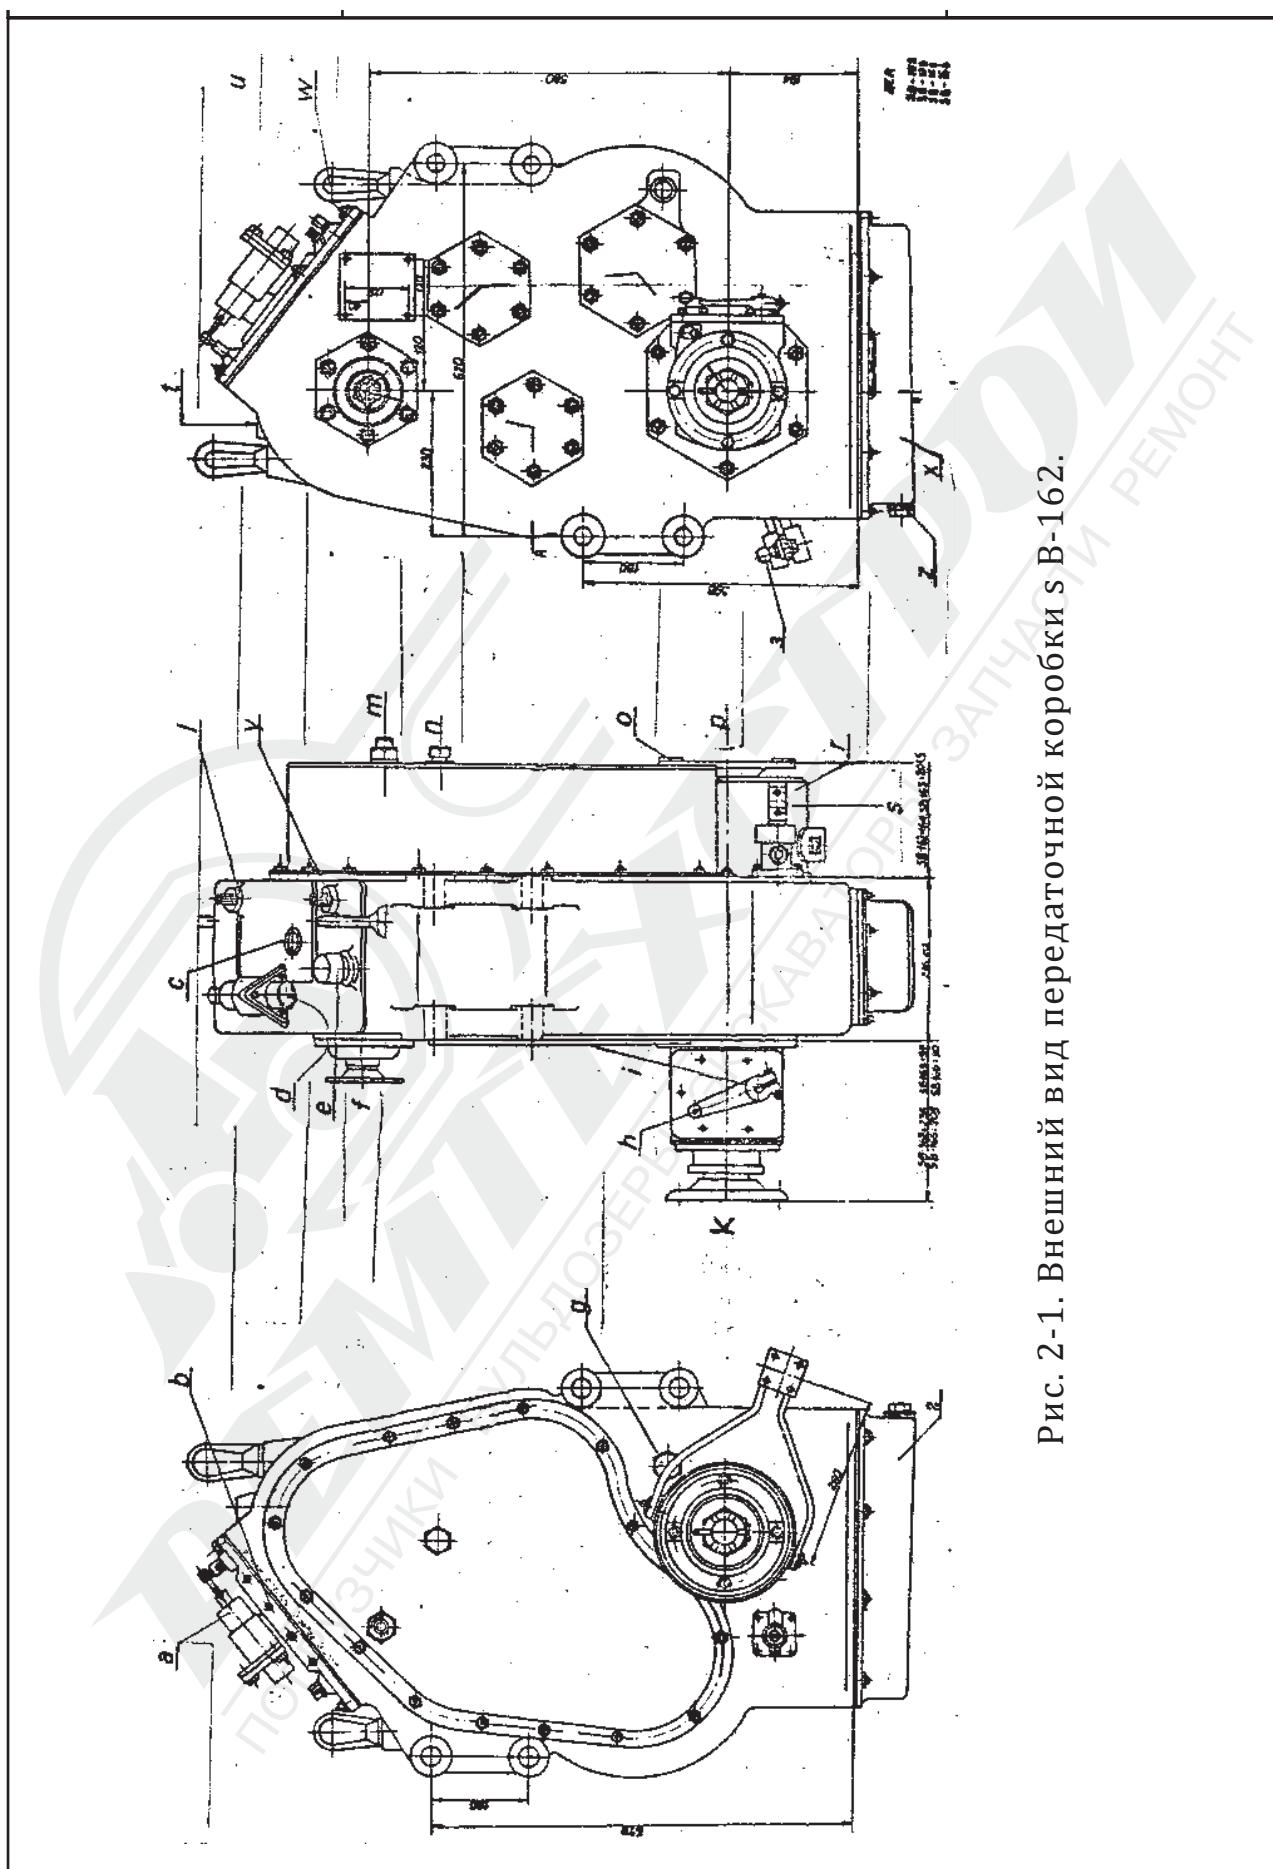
Внешний вид передаточной коробки с В-162.
